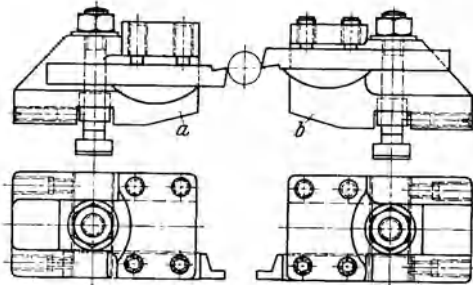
Plandrehstahlhalter für je zwei Stähle.
